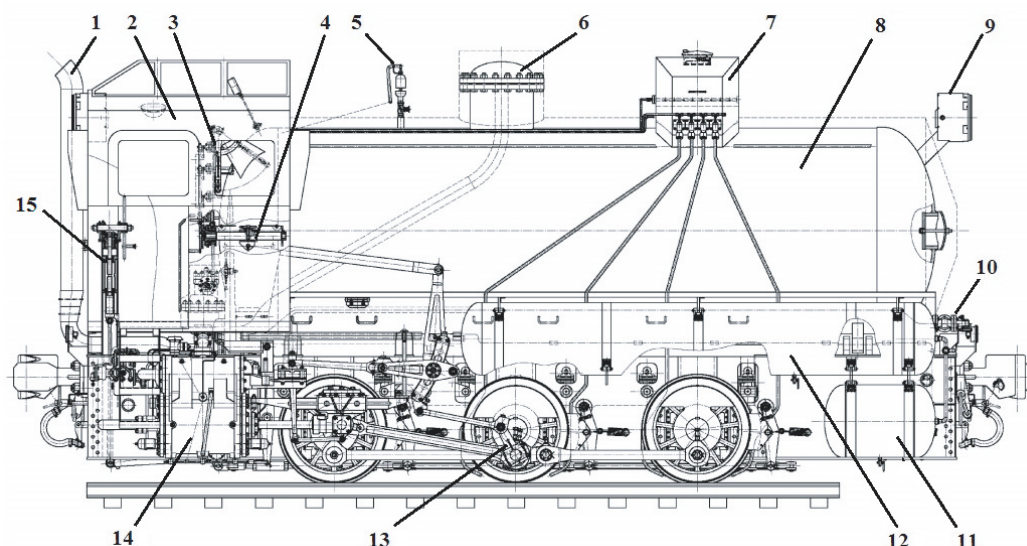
Общий вид локомотива ПАЛ-9П: 1 — паровыпускная труба; 2 — будка; 3 — регулятор; 4 — привод реверса; 5 — паровой свисток; 6 — сухопарник; 7 — песочница; 8 — котел-пароаккумулятор; 9 — прожектор; 10 — экипажировочный патрубок; 11 — запасной резервуар; 12 — главный резервуар; 13 — движущий механизм; 14 — паровой цилиндр; 15 — ручной тормоз
